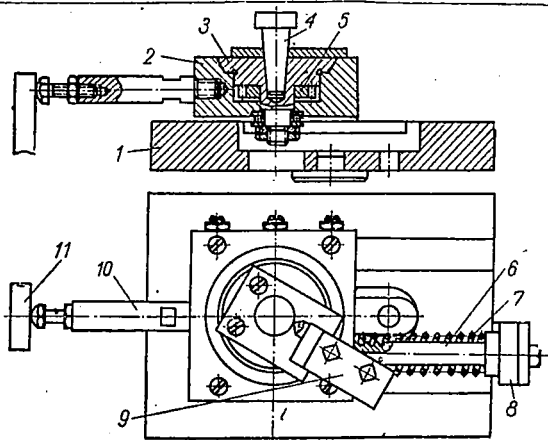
Приспособление с вращающимся столом для обработки сферических поверхностей.
